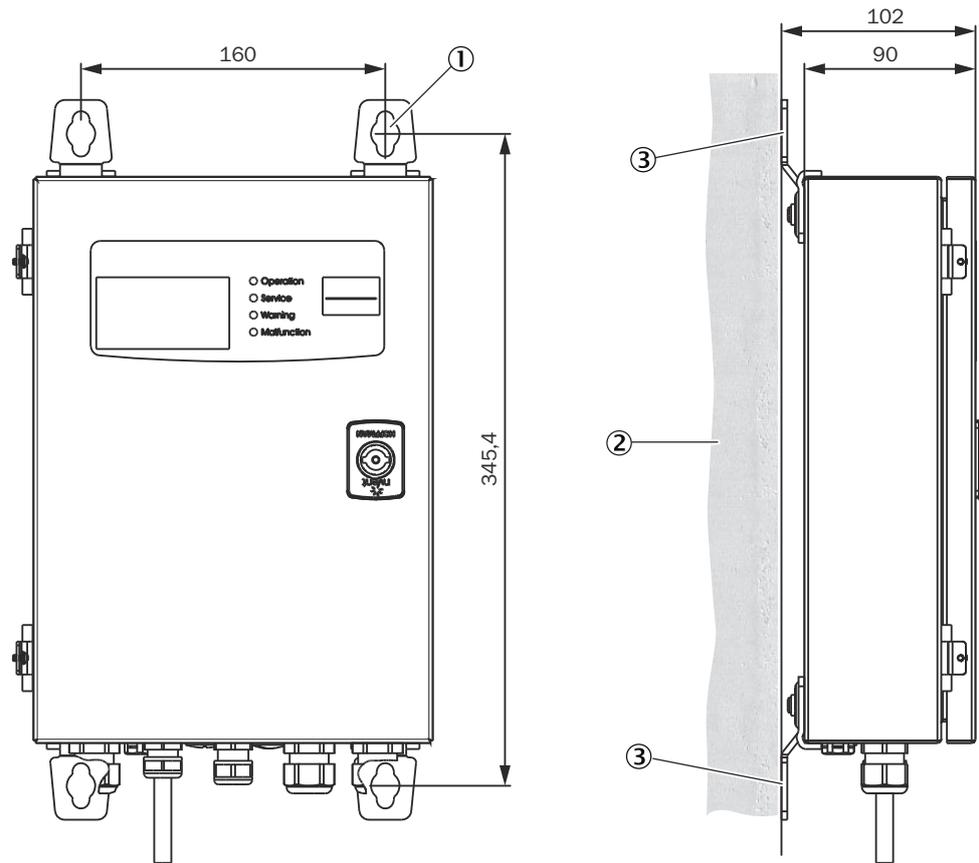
Montage Steuereinheit AWE Stahlblechgehäuse (Maße in mm)
